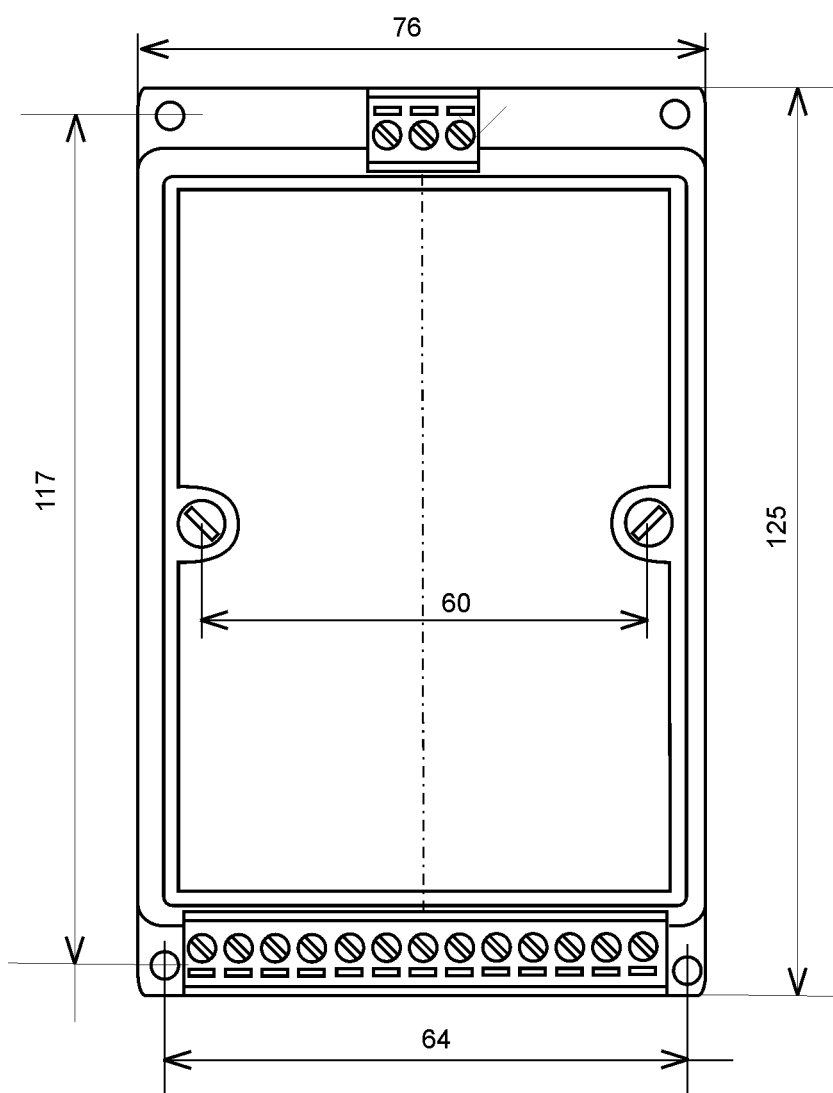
Габаритный чертеж и присоединительные размеры источника питания серии PS. Вид сверху
